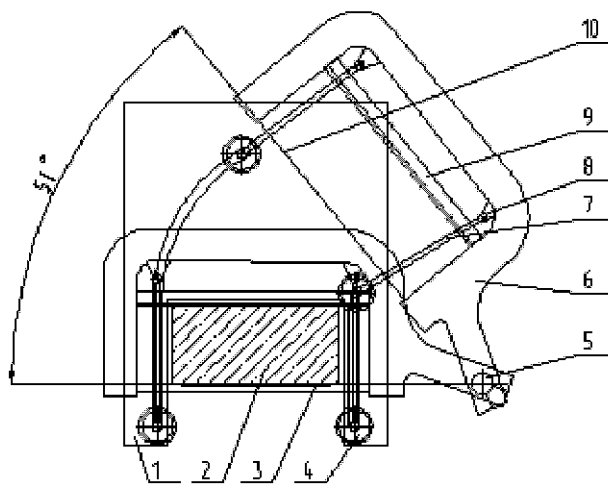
Схема работы смычкового механизма для резки кирпича-сырца со снятием фасок: 1 — пластина; 2 — глиняный брус; 3 — передаточный столик; 4 — ролик; 5 — смычковый вал; 6 — смычок; 7 — штанга; 8 — шарнирная опора; 9 — штанга (для заоваливания верхней кромки); 10 — струна.
